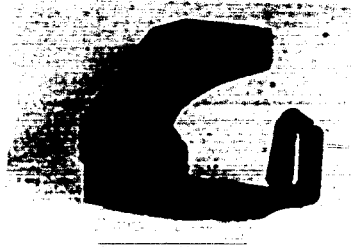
Gegenkontaktfeder für NSU-Motor Foto-Nr.35952
